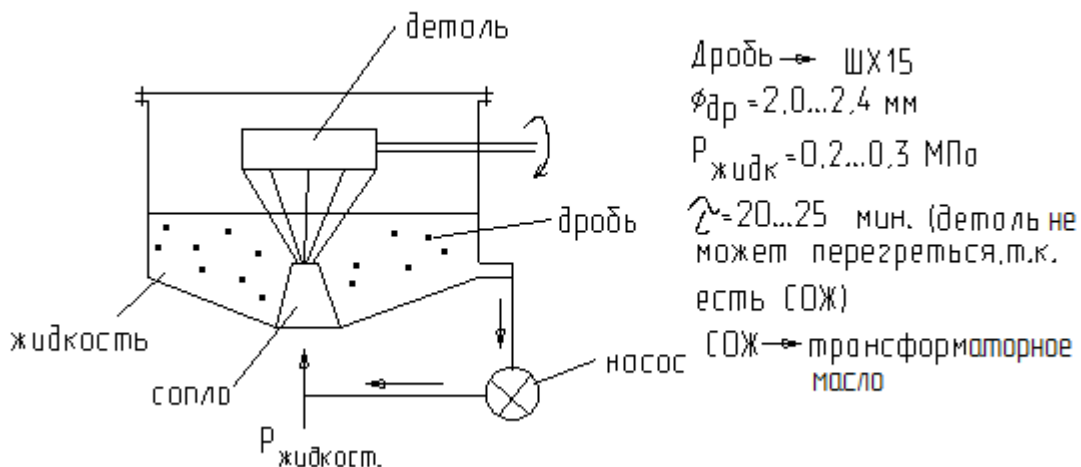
Схема установки для гидродробеструйной установки
